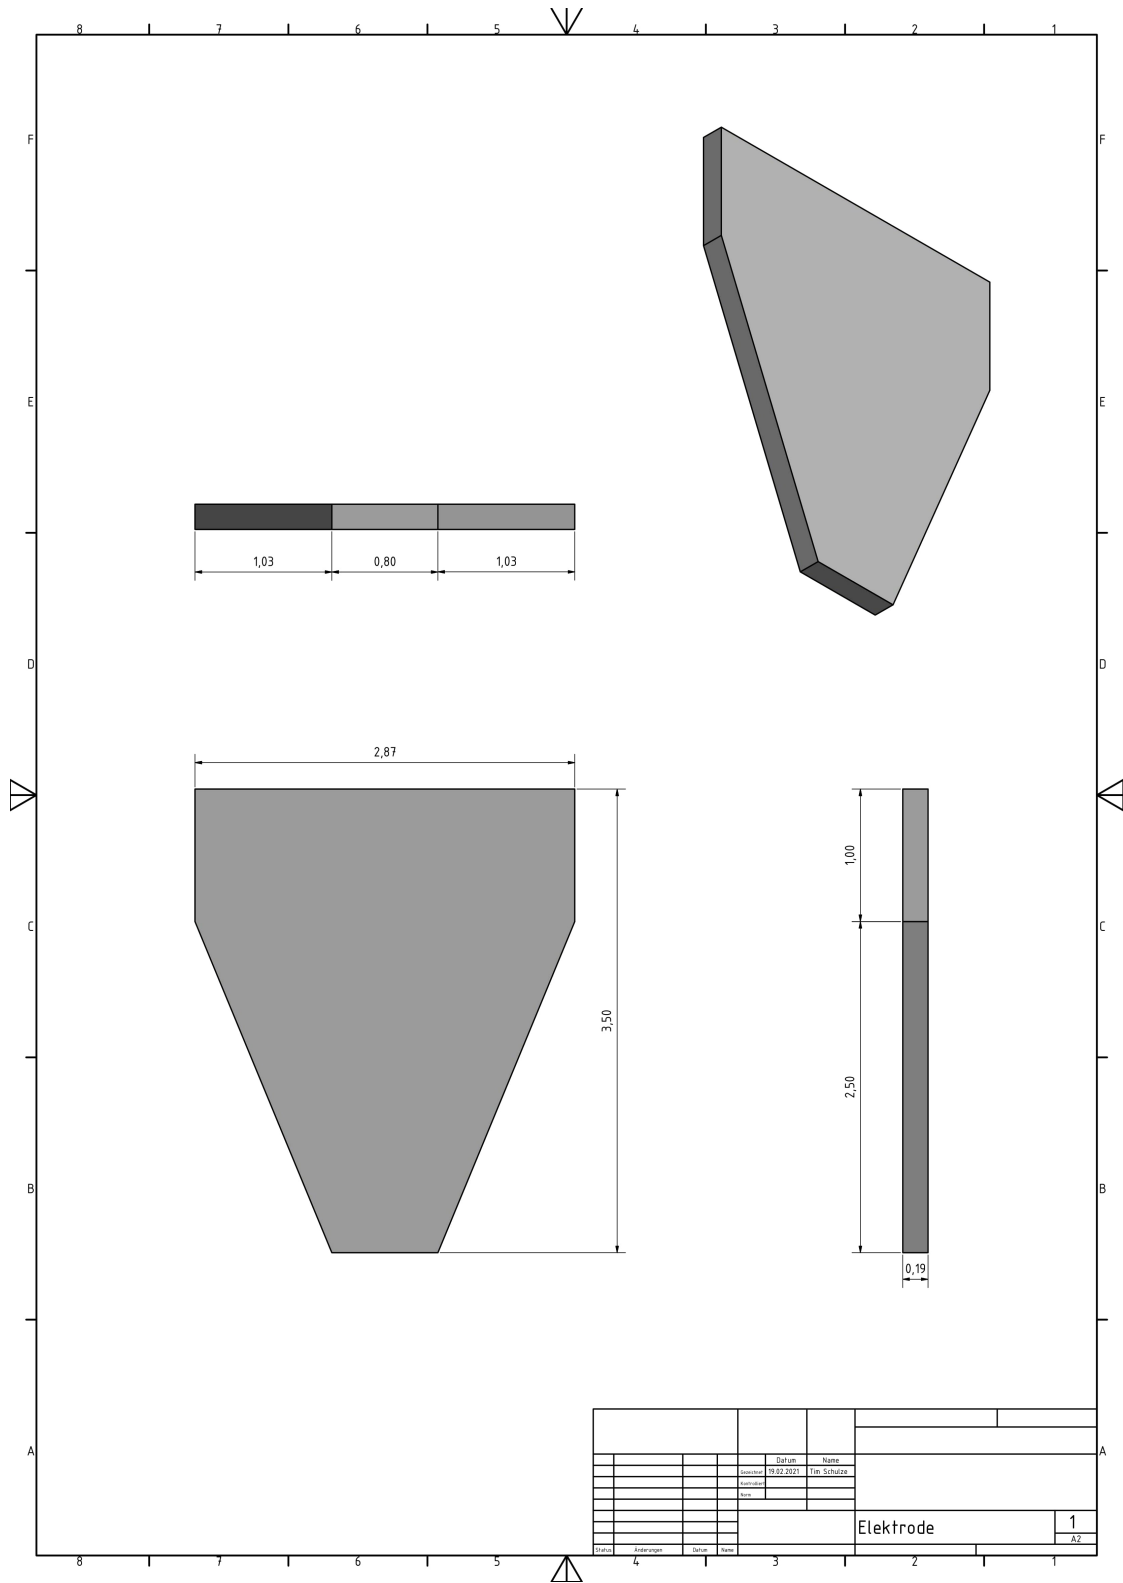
Technische Zeichnung der gedruckten Elektrode
